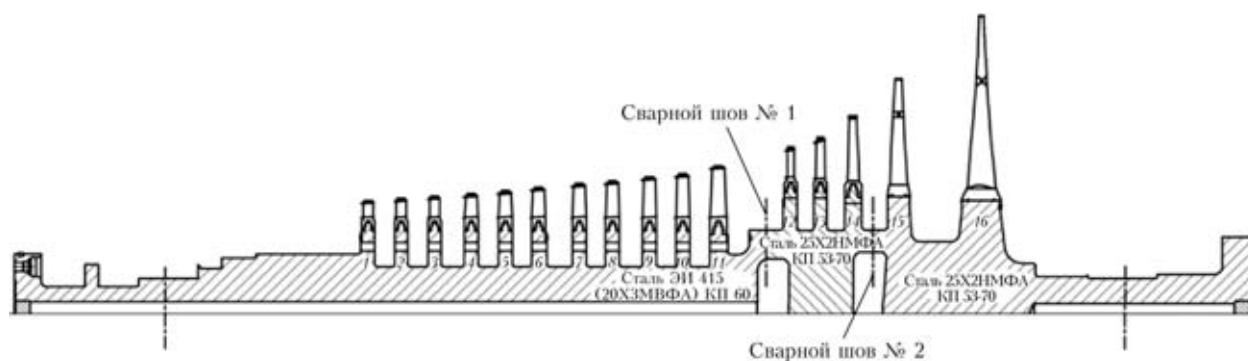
Эскиз продольного сечения сварного ротора ЦСД турбины мощностью 325 МВт
